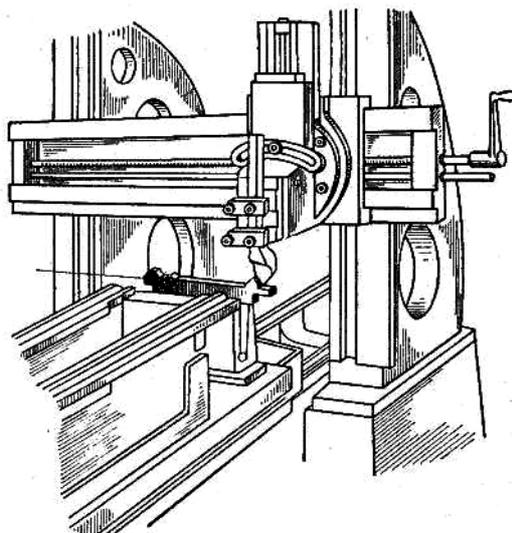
Приспособление для черновой обработки основания и направляющих станины станка
